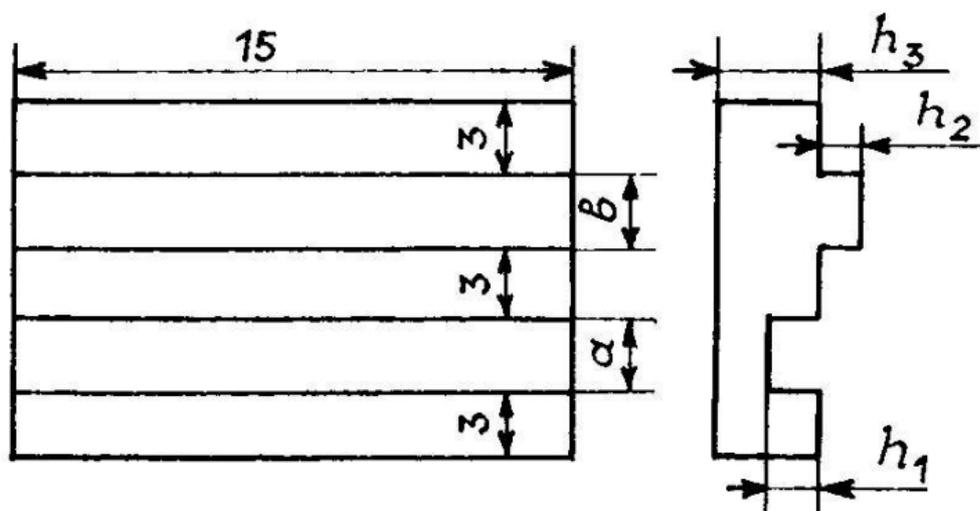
Образец-имитатор выпуклости и вогнутости сварного шва
